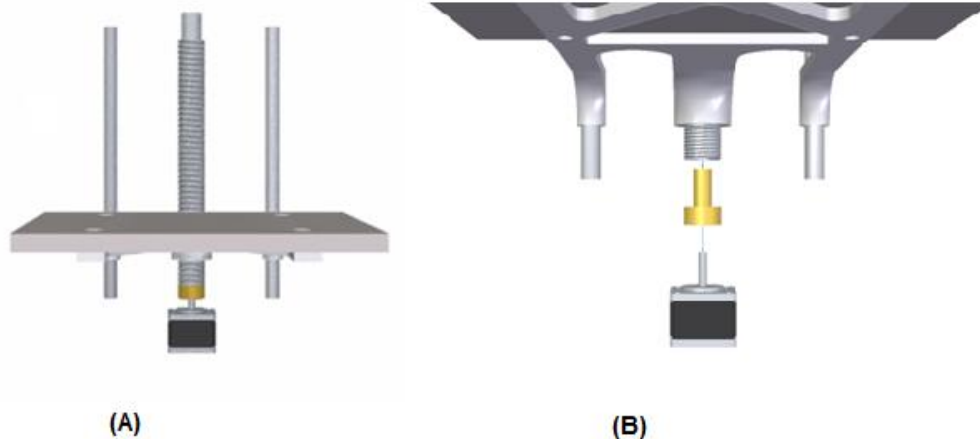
(A) Vista frontal del sistema del eje Z. (B) Vista explosionada de la zona motorizada del sistema del eje Z.
